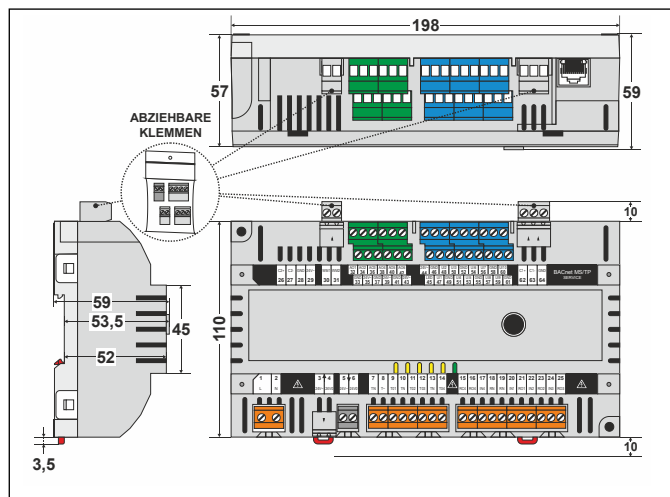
Dimensions du PCD7.LRL2 (en mm)
